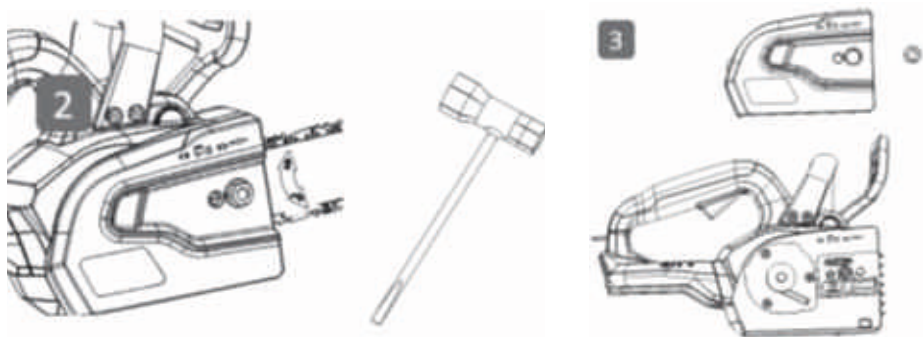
Поверните винт натяжки цепи по часовой стрелке, чтобы переместить натягивающую планку как можно ближе к ведущей звездочке.
